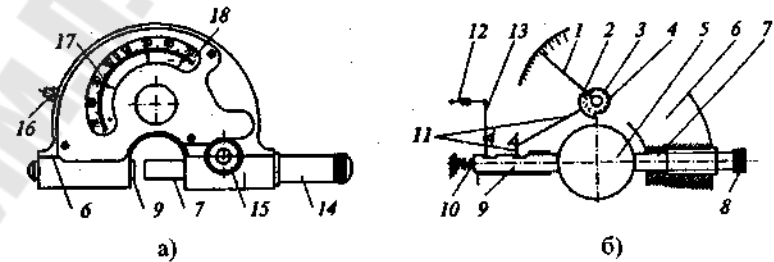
Рычажная скоба (а) и ее схема (б): 1 – стрелка; 2 – зубчатый сектор; 3 – спиральная пружина; 4 – зубчатое колесо; 5 – объект измерения; 6 – корпус; 7 – неподвижная (регулируемая) пятка; 8 – микровинт для настройки; 9 – подвижная пятка; 10 – пружина; 11 – измерительный рычаг; 12 – стержень арретира; 13 – рычаг арретира; 14 – предохранительный чехол; 15 – гайка фиксатора; 16 – кнопка арретира; 17 – шкала; 18 – указатель предела действительных отклонений
